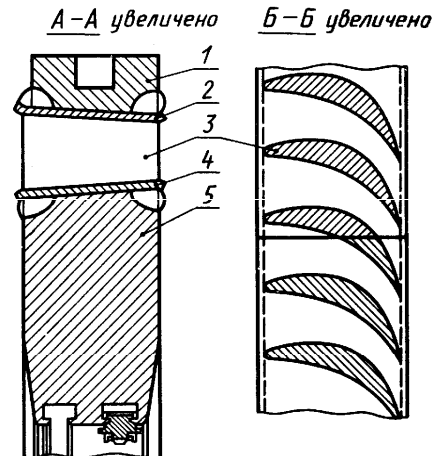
Сварные соединения направляющих лопаток с бандажной лентой и ободом
